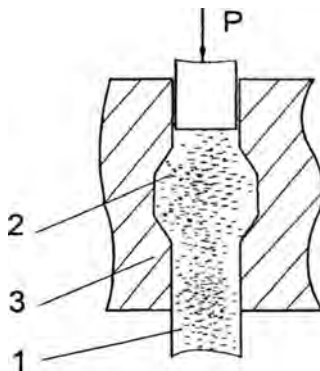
Схема процесса прессования длинномерных заготовок из порошка
